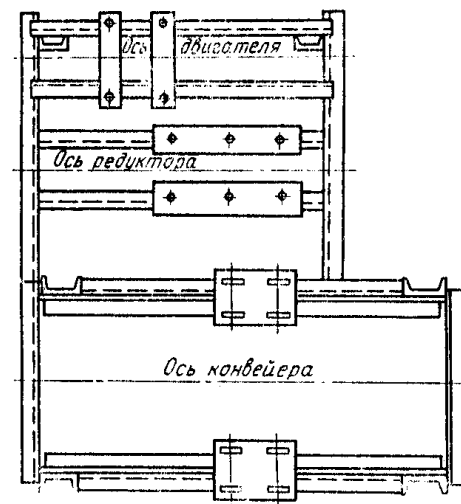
Пример опорной рамы приводного барабана и приводного механизма с цилиндрическим редуктором.
